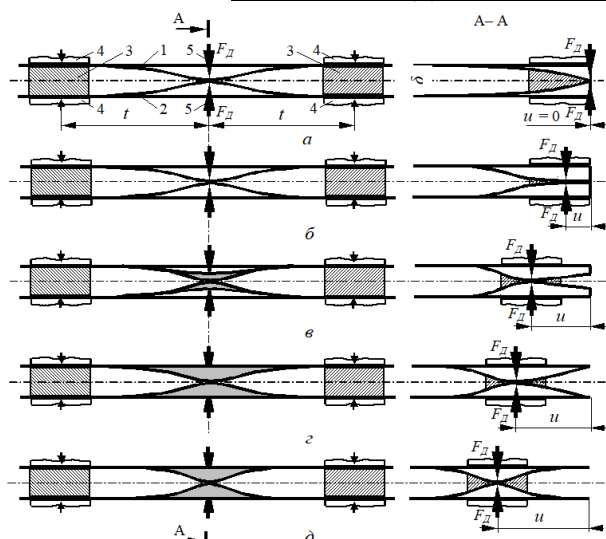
Схема деформації зварювальних деталей: 1, 2 – деталі; 3 – прокладка, що регулює величину зазору δ ; 4 – стискаючі струбцини;
